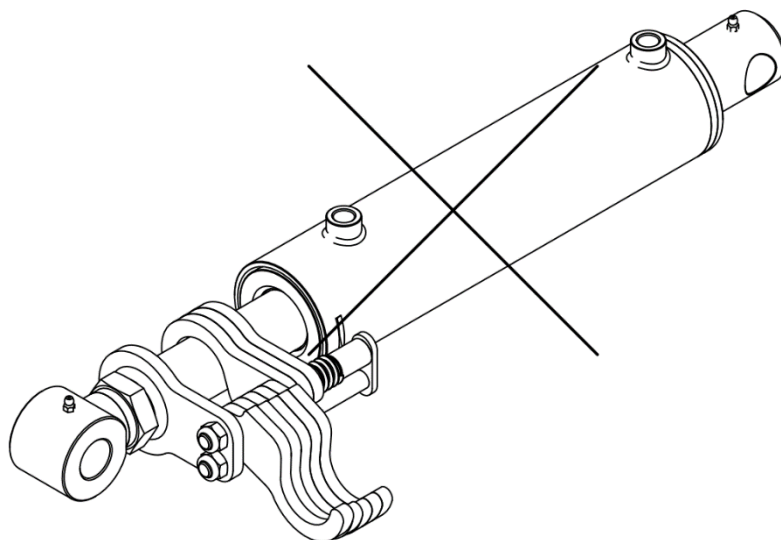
Installation incorrecte des cliquets sur la tige du piston du vérin. L'omission partielle de la fixation des cliquets à l'actionneur entraîne une répartition inégale des forces agissant sur la tige du piston et peut conduire à un flambage de la tige du piston et endommager l'ensemble du vérin. Une telle installation des cliquets est inadmissible !
